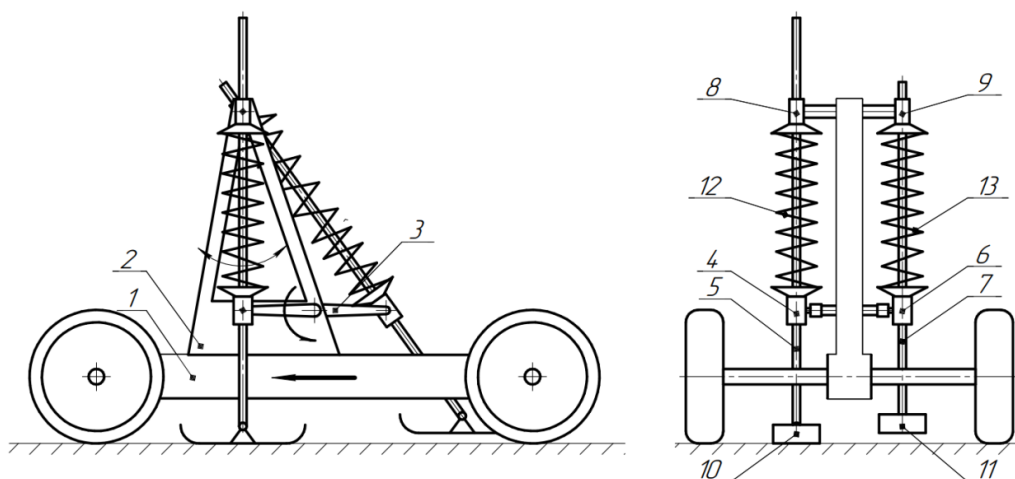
Колесно-шагающий движитель с цикловым механизмом
